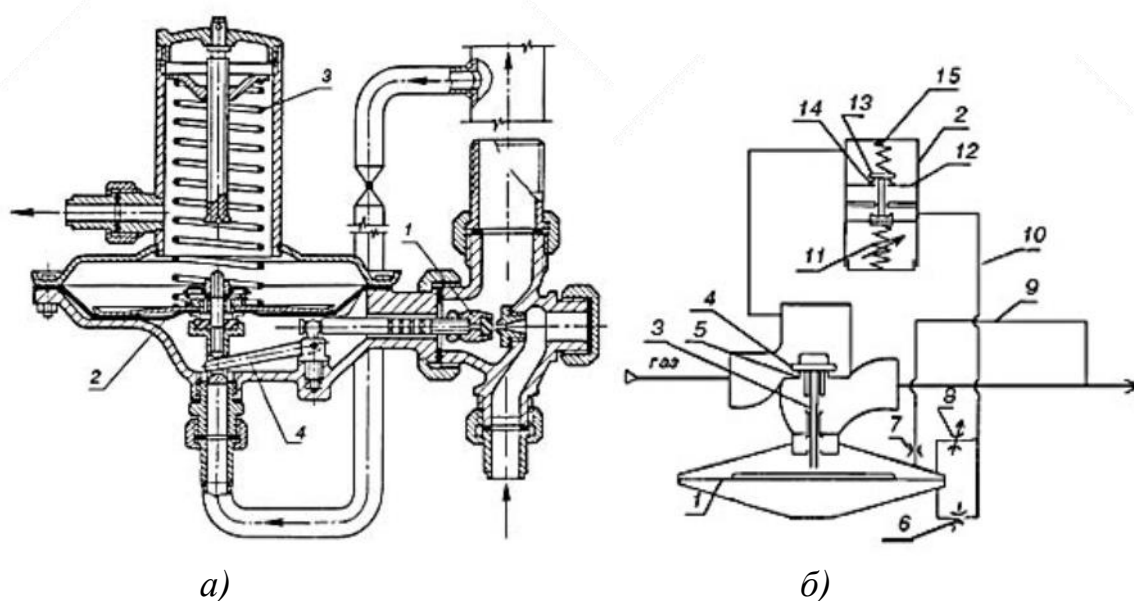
а) регулятор с рычажной передачей: 1 — регулирующий клапан; 2 — рабочая мембрана; 3 — настроечная пружина; 4 — коленчатый рычаг; б) регулятор с пилотом: 1 — мембрана; 2 — пилот (регулятор управления); 3 — шток; 4 — клапан; 5 — седло; 6, 7, 8 — регулируемые дроссели; 9, 10 — импульсные трубопроводы; 11 — регулировочная пружина пилота; 12 — мембрана пилота; 13 — клапан пилота; 14 — седло; 15 — возвратная пружина.
